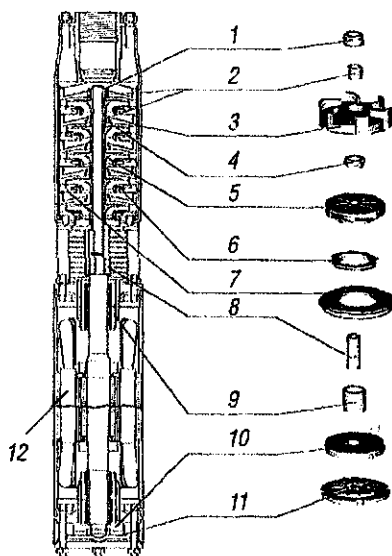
Схема погружного скважинного насоса типа ЭЦВ: 1 – верхний подшипник; 2 – распорная втулка; 3 – лопаточный отвод; 4 – втулка лопаточного отвода; 5 – рабочее колесо; 6 – втулка диафрагмы; 7 – диафрагма; 8 – муфта; 9 – подшипник; 10 – пята; 11 – упорный подшипник; 12 – электродвигатель
